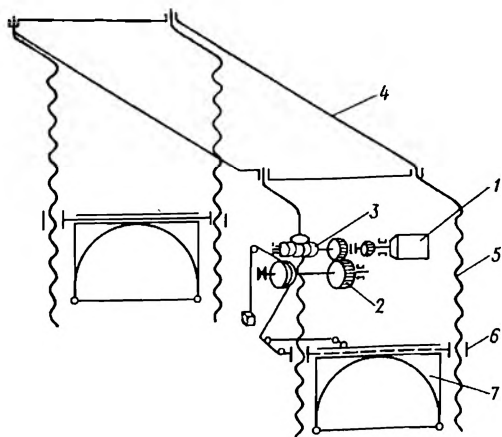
Кинематическая схема привода подачи распиловочного маятникового станка модели К-3М
